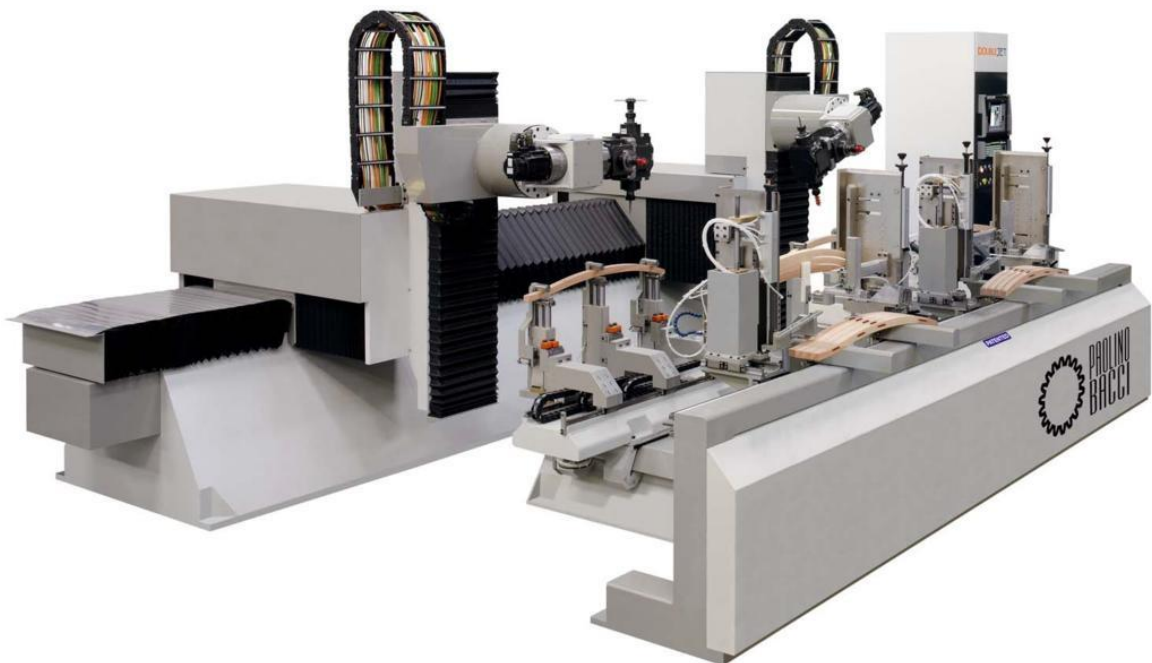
CNC obráběcí stroj SHARP (Bacci, © 2005a, dodatečně upraveno)
